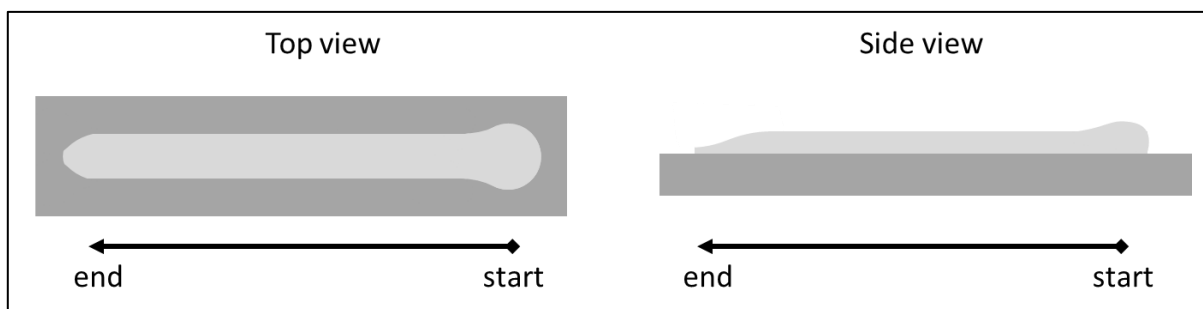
Vue de haut et de côté d'un cordon de soudure
